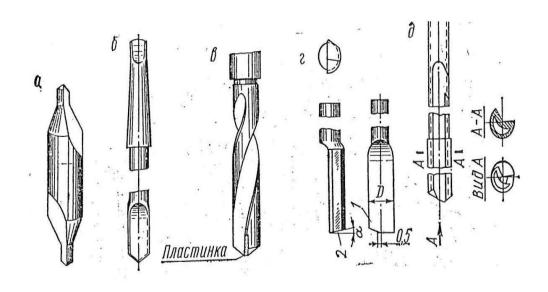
Свёрла: а — центровочное; б — перовое; в — спиральное с пластинкой из твердого сплава; г, д — для глубокого сверления
